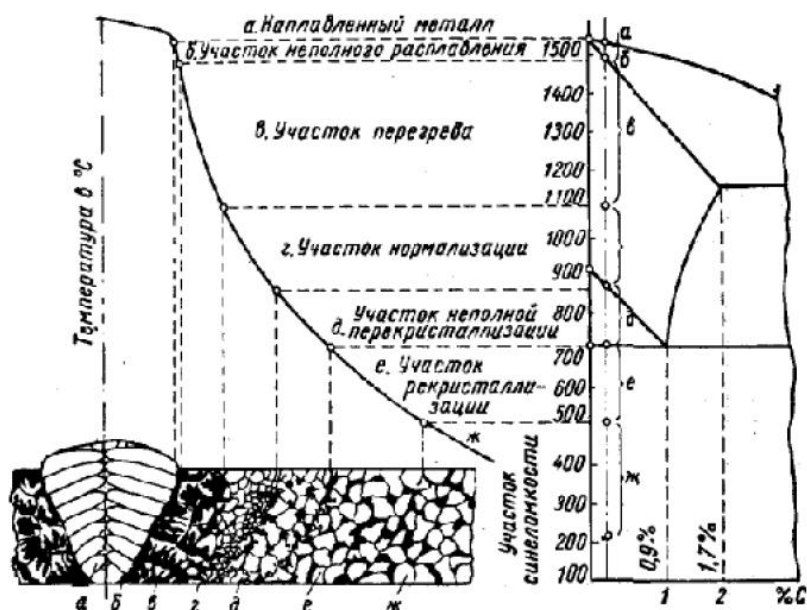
Структурная схема сварного шва для стали 20 [6]
